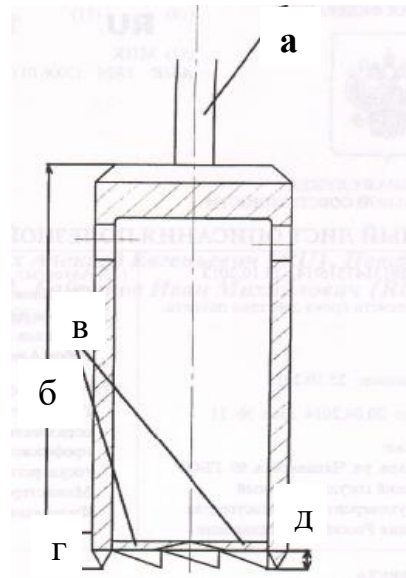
а. Схематическое изображение спиралевидной фрезы: а – держатель фрезы; б – рабочая часть; в, г, д – резцы
